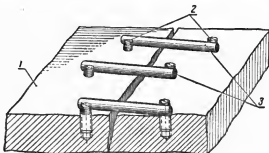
Подготовка толстостенной детали к заварке трещины:
